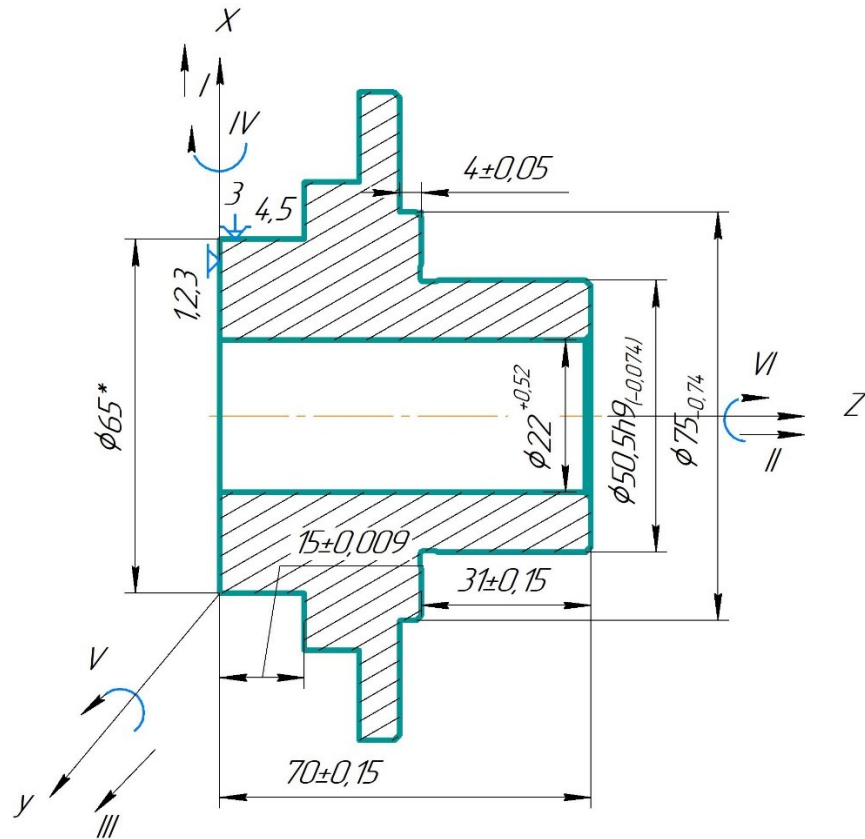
Схема базування заготовки по діаметру 65 мм і прилеглому торцю  $15_{-0,09}$  мм.
